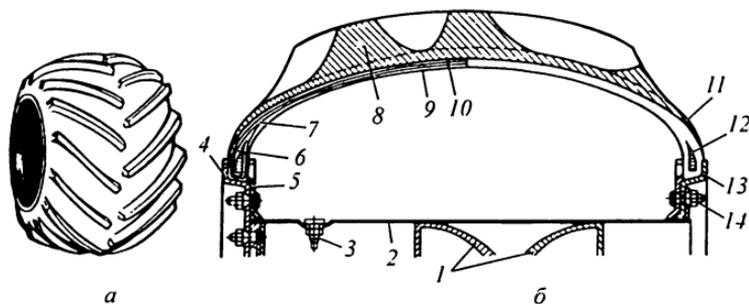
Арочная шина: *а* — внешний вид; *б* — поперечное сечение; 1 — диск колеса; 2 — обод; 3 — вентиль; 4 — наружное бортовое кольцо; 5 — внутреннее бортовое кольцо; 6 — борт; 7 — каркас; 8 — протектор; 9 — герметизирующий слой; 10 — брекер; 11 — боковина; 12 — бортовое кольцо; 13 — полка наружного бортового кольца; 14 — стяжной болт
